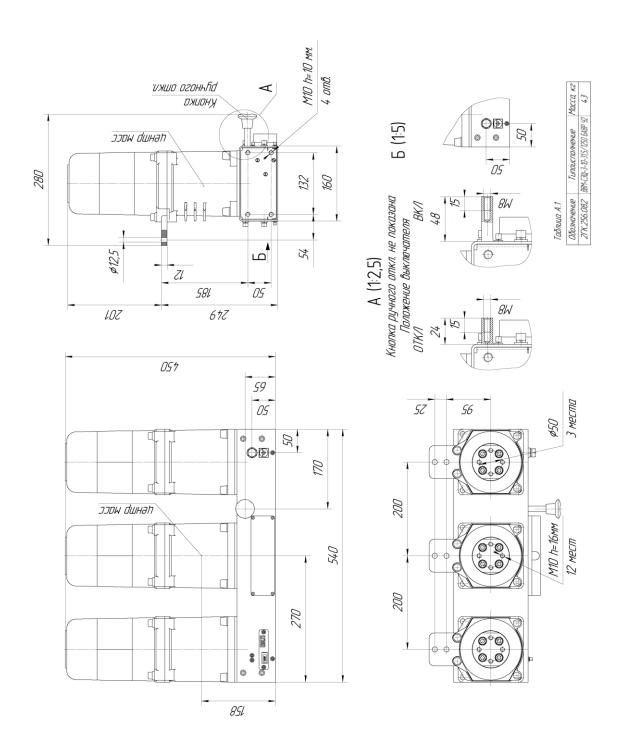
Габаритные, присоединительные и установочные размеры выключателя типа ВВМ-СЭЩ-3-10-31,5/1250 БАВР У2
